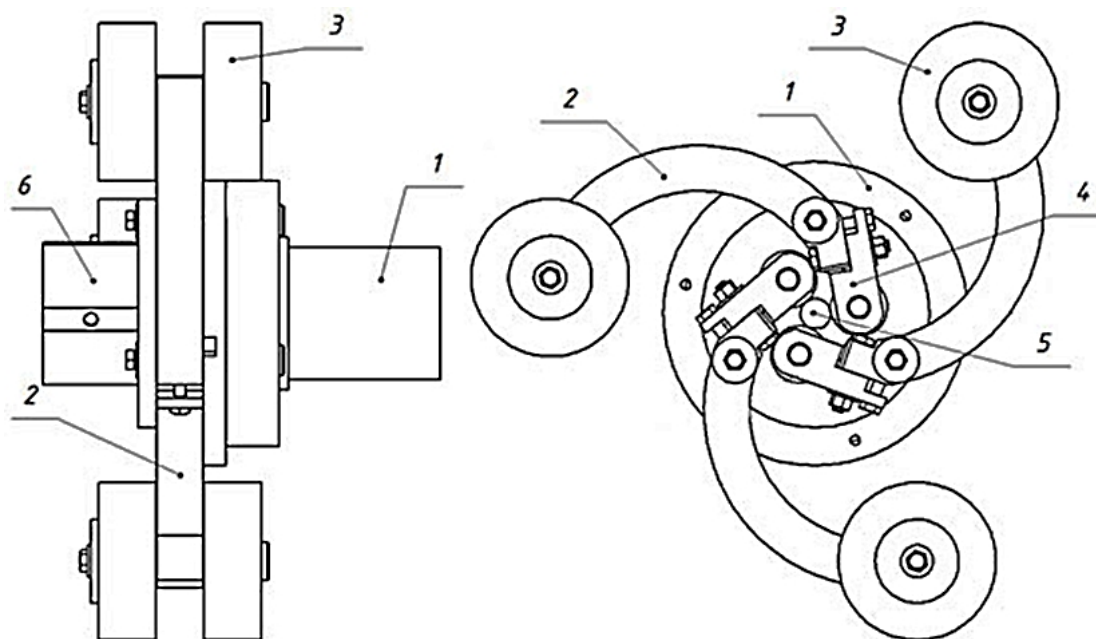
Центробежный обкатник: 1 – корпус; 2 – рычаг; 3 – груз; 4 – державка с деформирующим роликом; 5 – обкатываемая деталь; 6 – дополнительная опора (защитный кожух убран)
